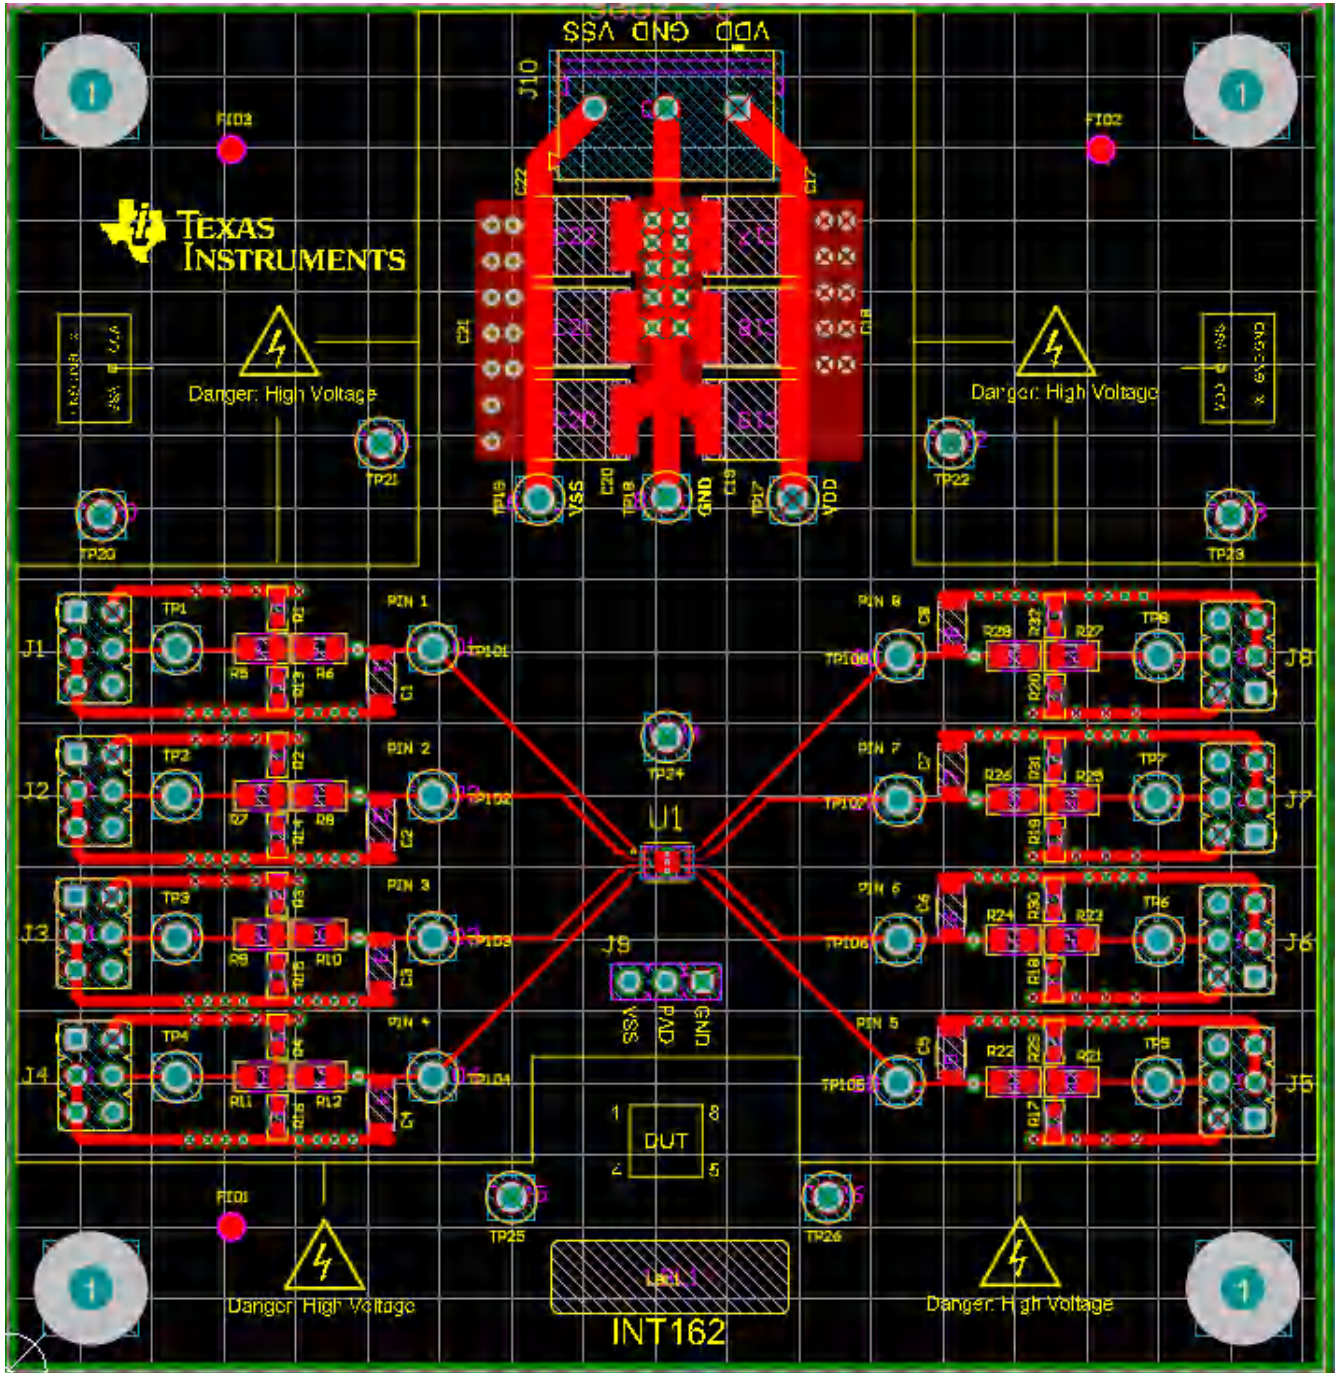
PCB 顶层 TMUX-8RQX-EVM
